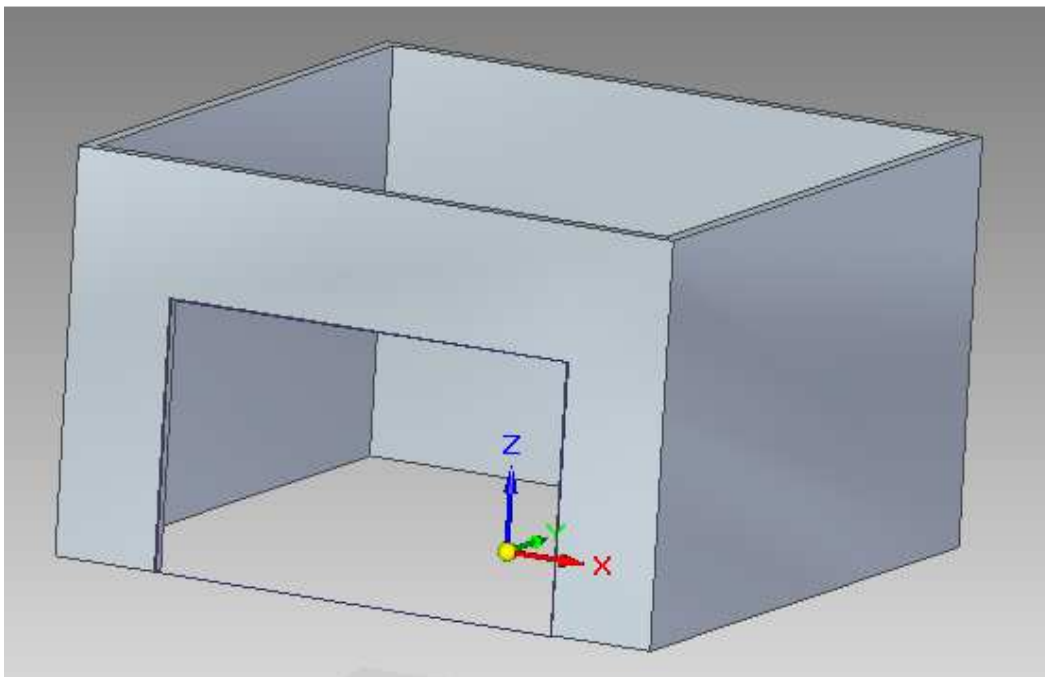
CUBO TELESCÓPICO SUPERIOR
